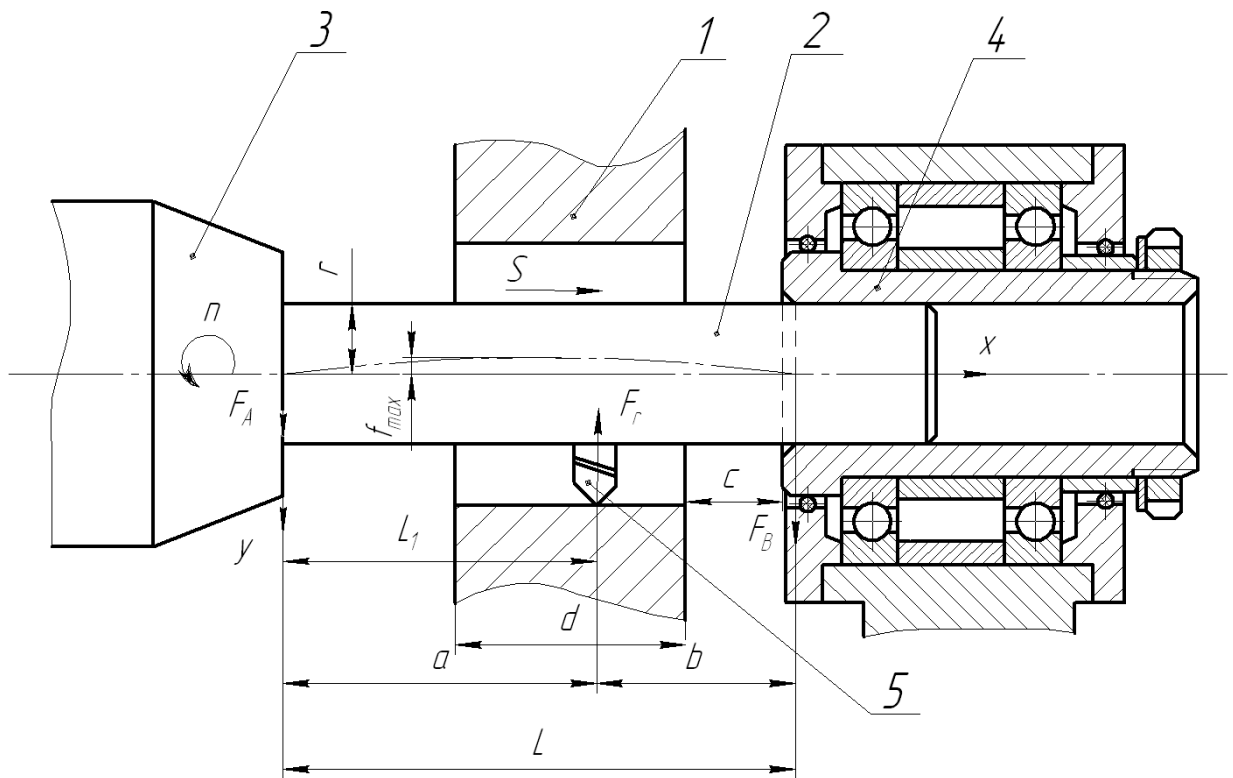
Розрахункова схема для визначення величини деформації оправки під час розточування наскрізного отвору із застосуванням додаткової обертової втулки: 1 – заготовка; 2 – оправка для розточування; 3 – шпиндель верстата; 4 – додаткова обертова втулка; 5 – різець для розточування
